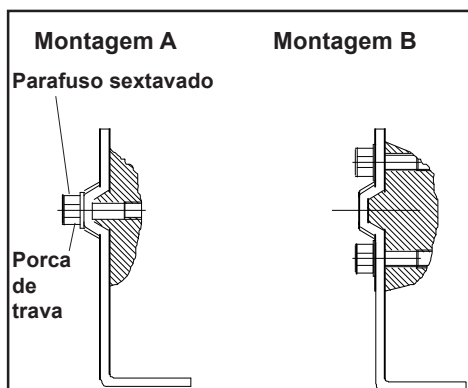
Montagem de atuador de forquilha (segundo IEC 534 parte 6)
